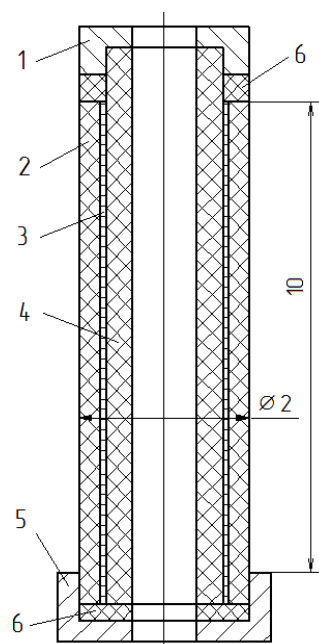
Схема конструкции трубчатого микро ТОТЭ
